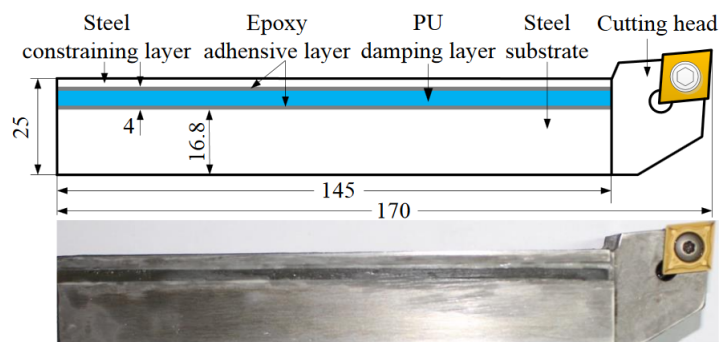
Conception du porte-outil pour le tournage [8].
